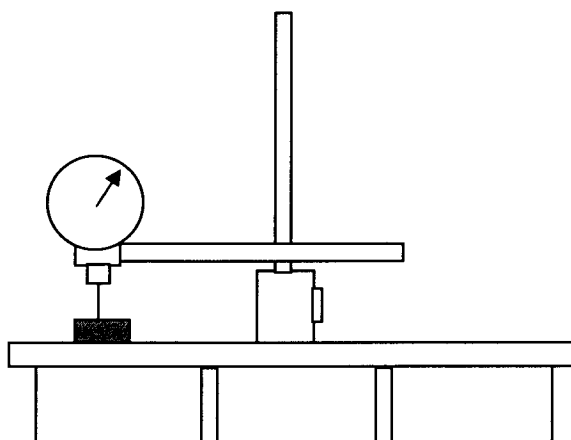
Установка меры для проверки глубины плоскодонных отверстий.
